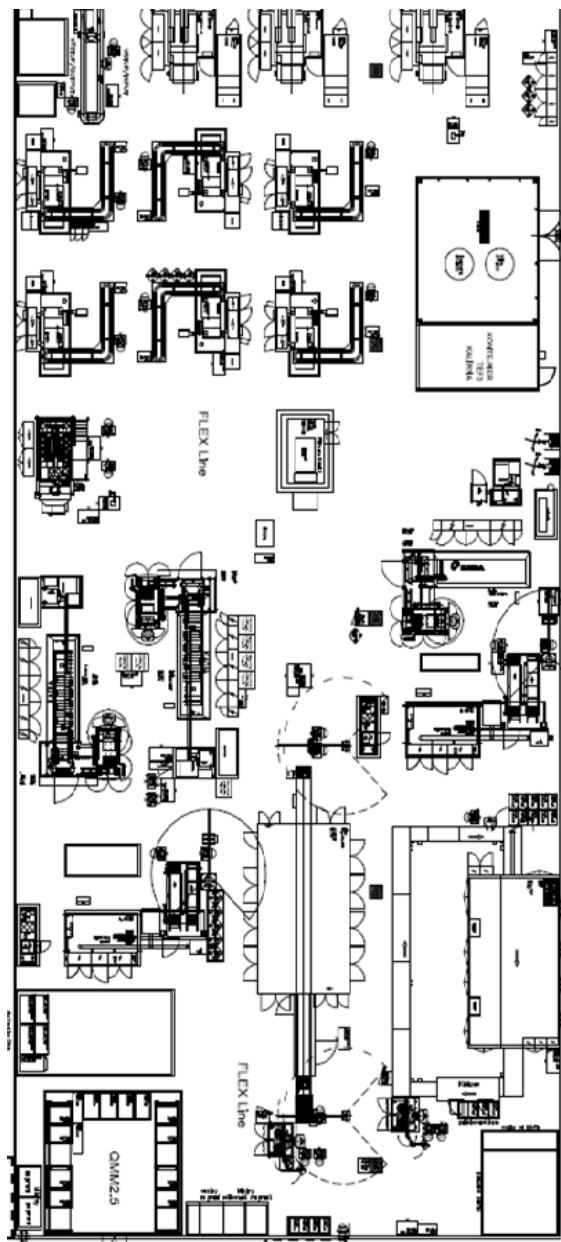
Aktuální uspořádání strojů pro obrábění po tepelném zpracování na hale 301.
